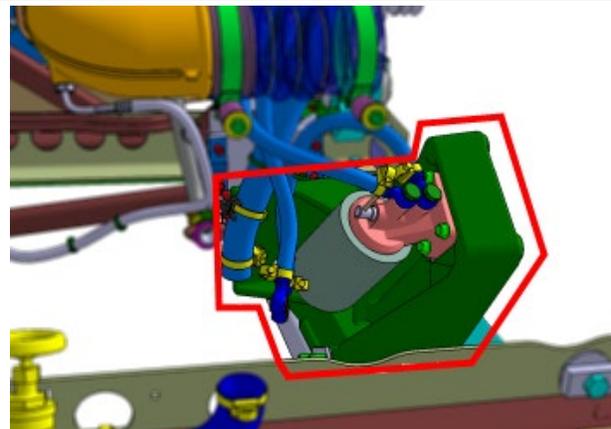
SUPPORT ARRIÈRE GAUCHE DE MOTEUR
